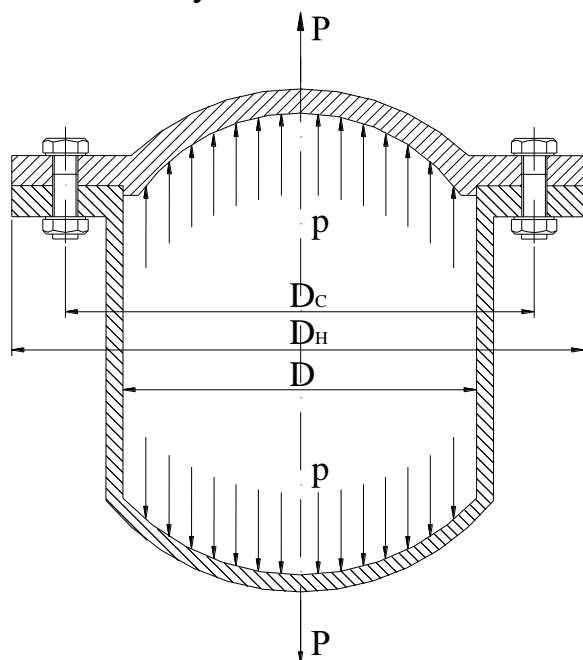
Крепление крышки резервуаров с внутренним давлением
